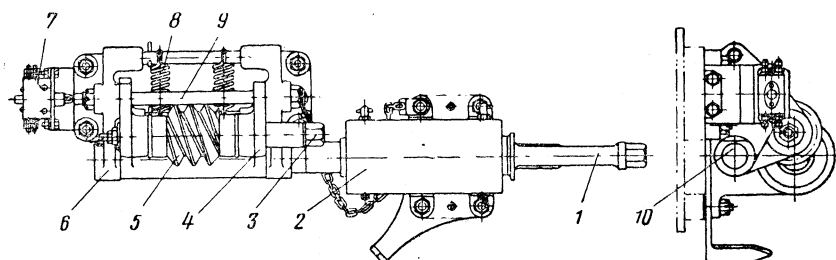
Валоповоротный механизм коленчатых валов дизеля 2Д100:
